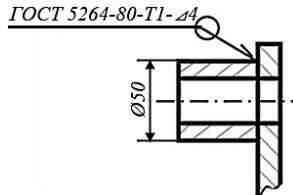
Сварное соединение, полученное ручной дуговой сваркой
